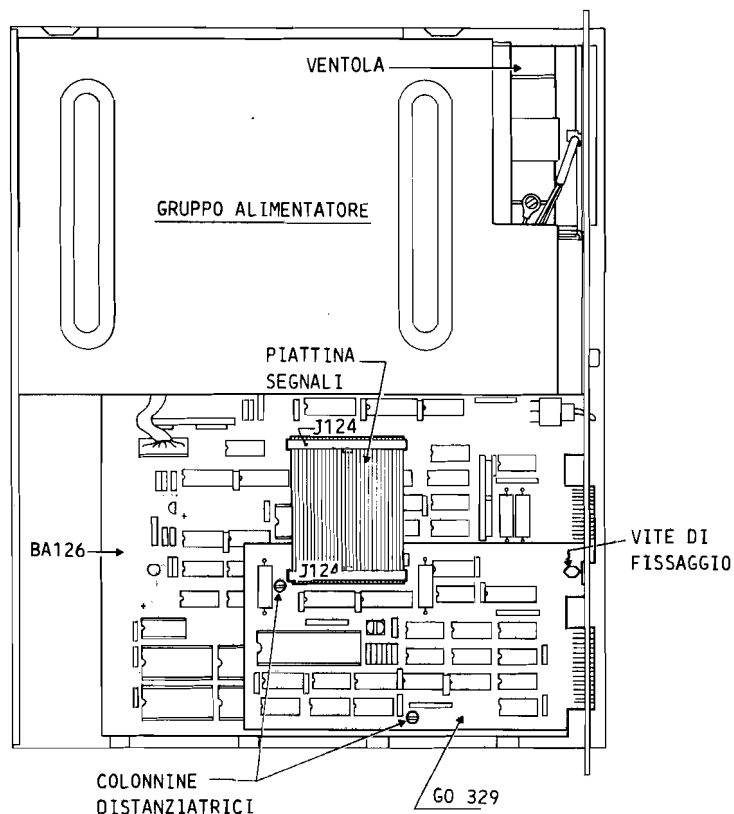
Montaggio piastra opzione per pin pad e badge reader
